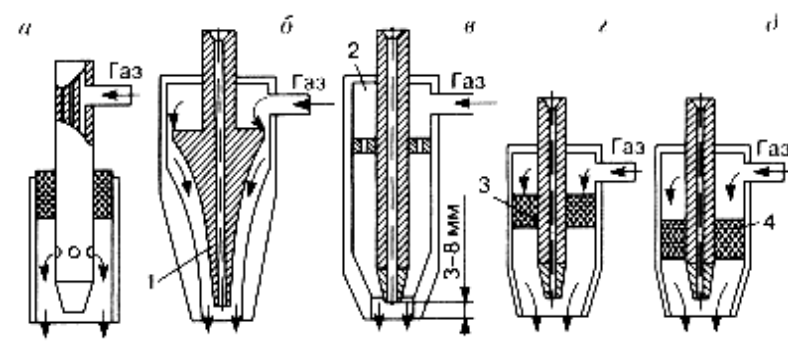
Схемы подвода газа в сварочных горелках[21]: а - с кольцевым подводом газа; б-е отражателями; в - с успокоительными камерами; г - с сеточными вставками; д - с металлокерамическими вставками (1 - отражатель газа; 2 - успокоительная камера; 3 - сетка; 4 - металлокерамика)
